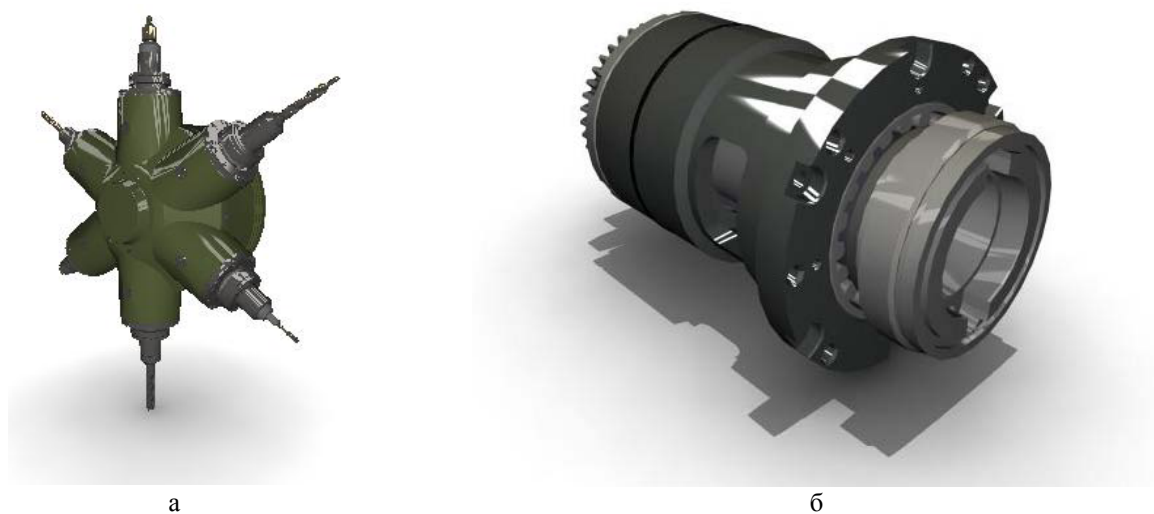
Рендеринг ШРГ: а – сборка; б – шпиндельный узел
